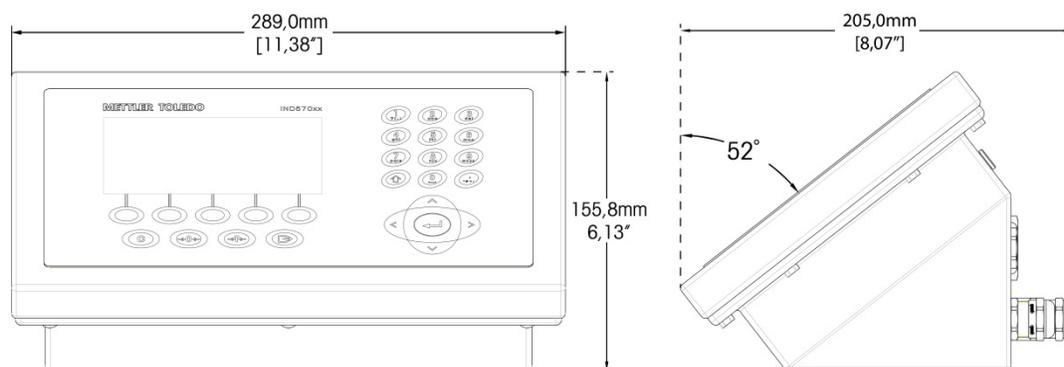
Dimensões do gabinete para ambiente adverso IND570 com suportes de montagem de ângulo fixo, montagem VESA
